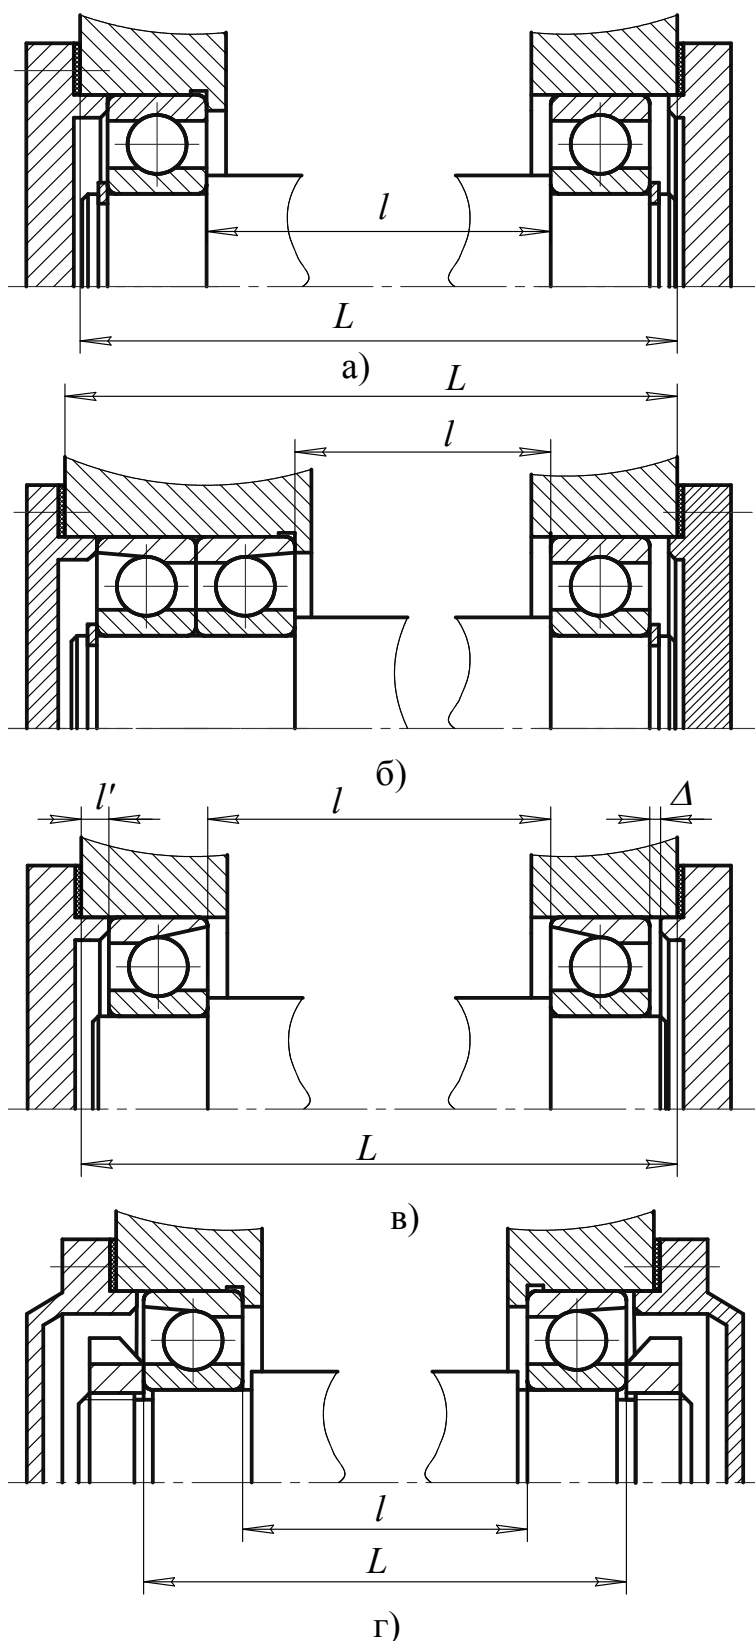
Варианты конструкции опор подшипникового узла
